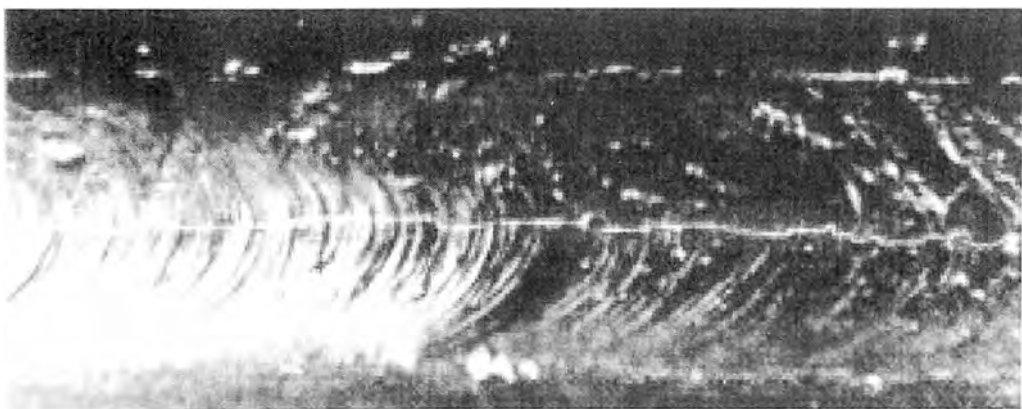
Fisura en la garganta en la raíz de una soldadura de filete
